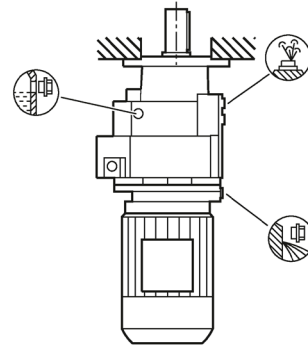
Einbaulagen für Stirradgetriebe DF/ZF Flanschsführung und DZ/ZZ mit Gehäuseflansch, Baugrößen 19 - 29
